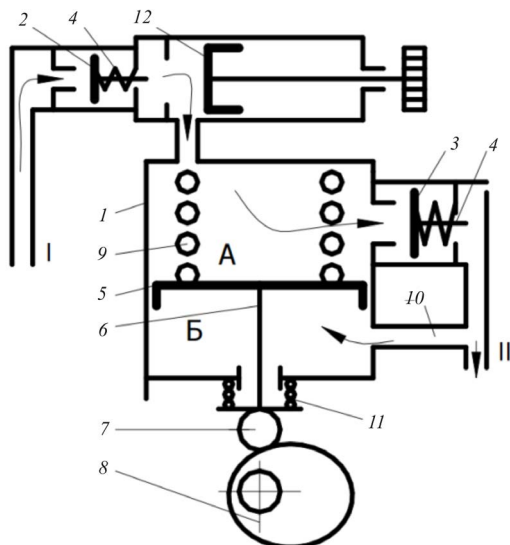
Схема плунжерного топливоподкачивающего насоса: 1 – корпус; 2 – впускной клапан; 3 – выпускной клапан; 4 – пружина клапана; 5 – плунжер; 6 – толкатель; 7 – ролик толкателя; 8 – эксцентрик; 9, 11 – пружины; 10 – перепускной канал; 12 – насос ручной подкачки; I – впускной канал; II – нагнетательный канал; А – надплунжерная полость; Б – подплунжерная полость
